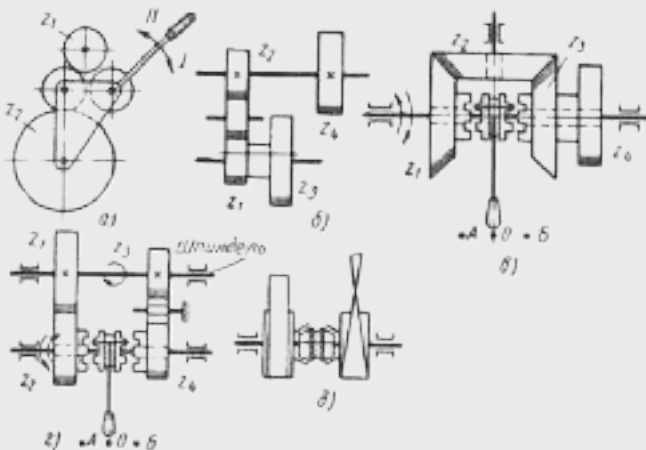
Схеми реверсивних механізмів: а — трензель з циліндричними зубчастими колесами; б — схема реверсивного механізму з переміщуваними на шліцьовому валі зубчастими колесами; в, г — реверсування здійснюють за допомогою двосторонньої кулачкової муфти; д — ремінна реверсивна передача
